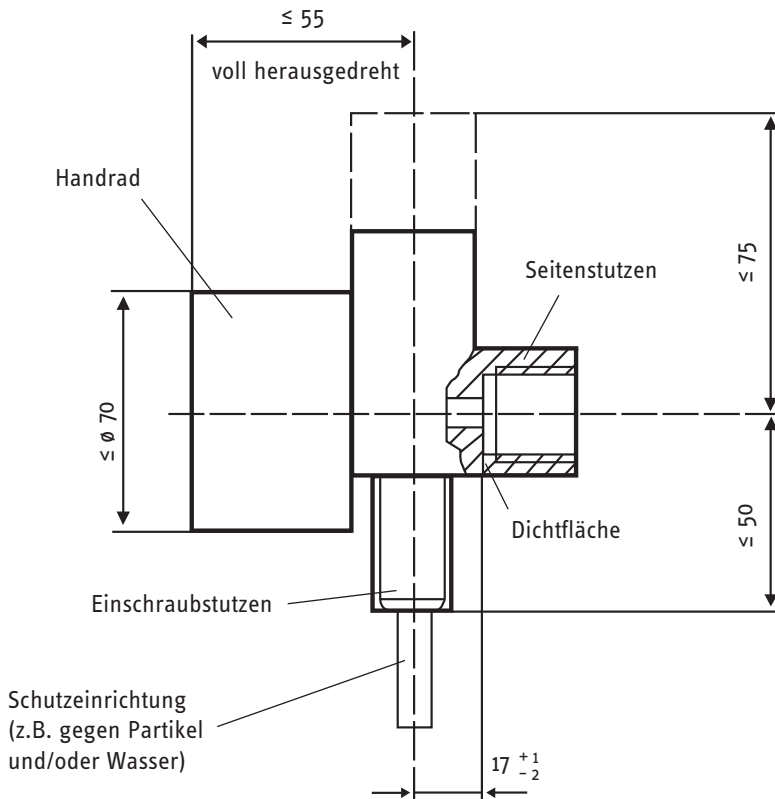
Gasflaschenventil Typ 2 (alle Maße in mm)
